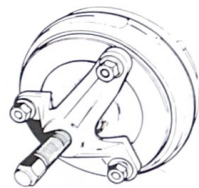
Extractor para sacar el tambor de freno trasero con el rodamiento.
